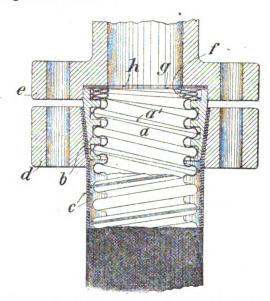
Endverbindung für geschweißte Metallschläuche.
